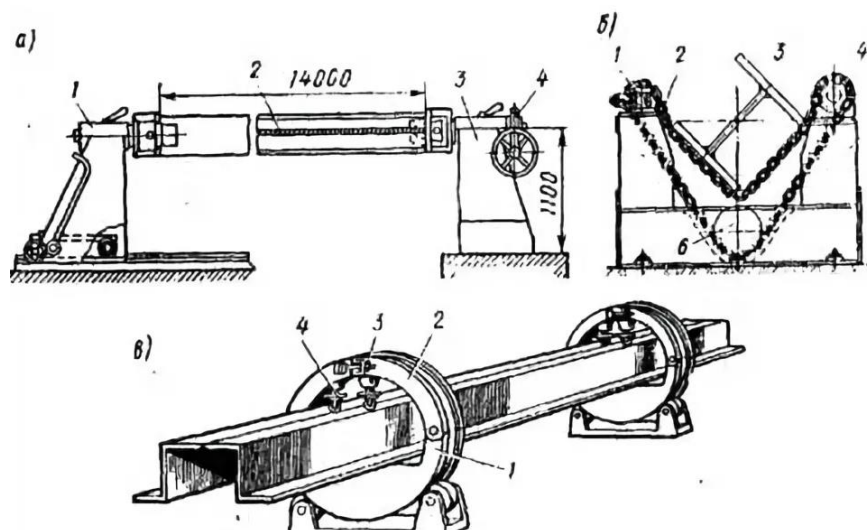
Схема позиционеров-кантователей для сварки балок
